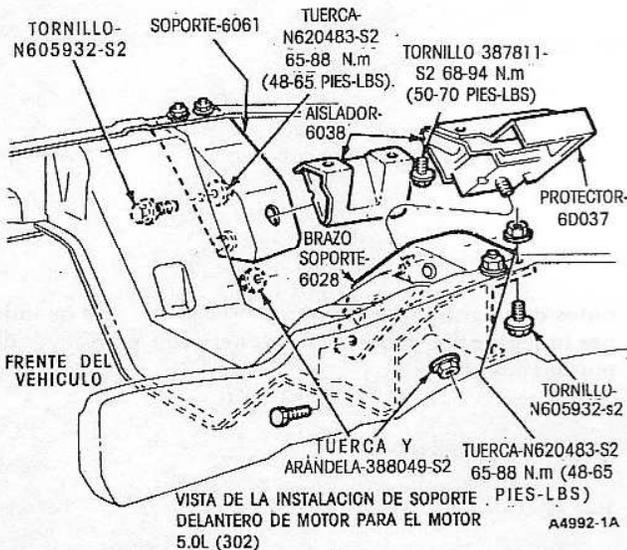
Soporte Delantero de Motor—F-100, F-250—Bronco
